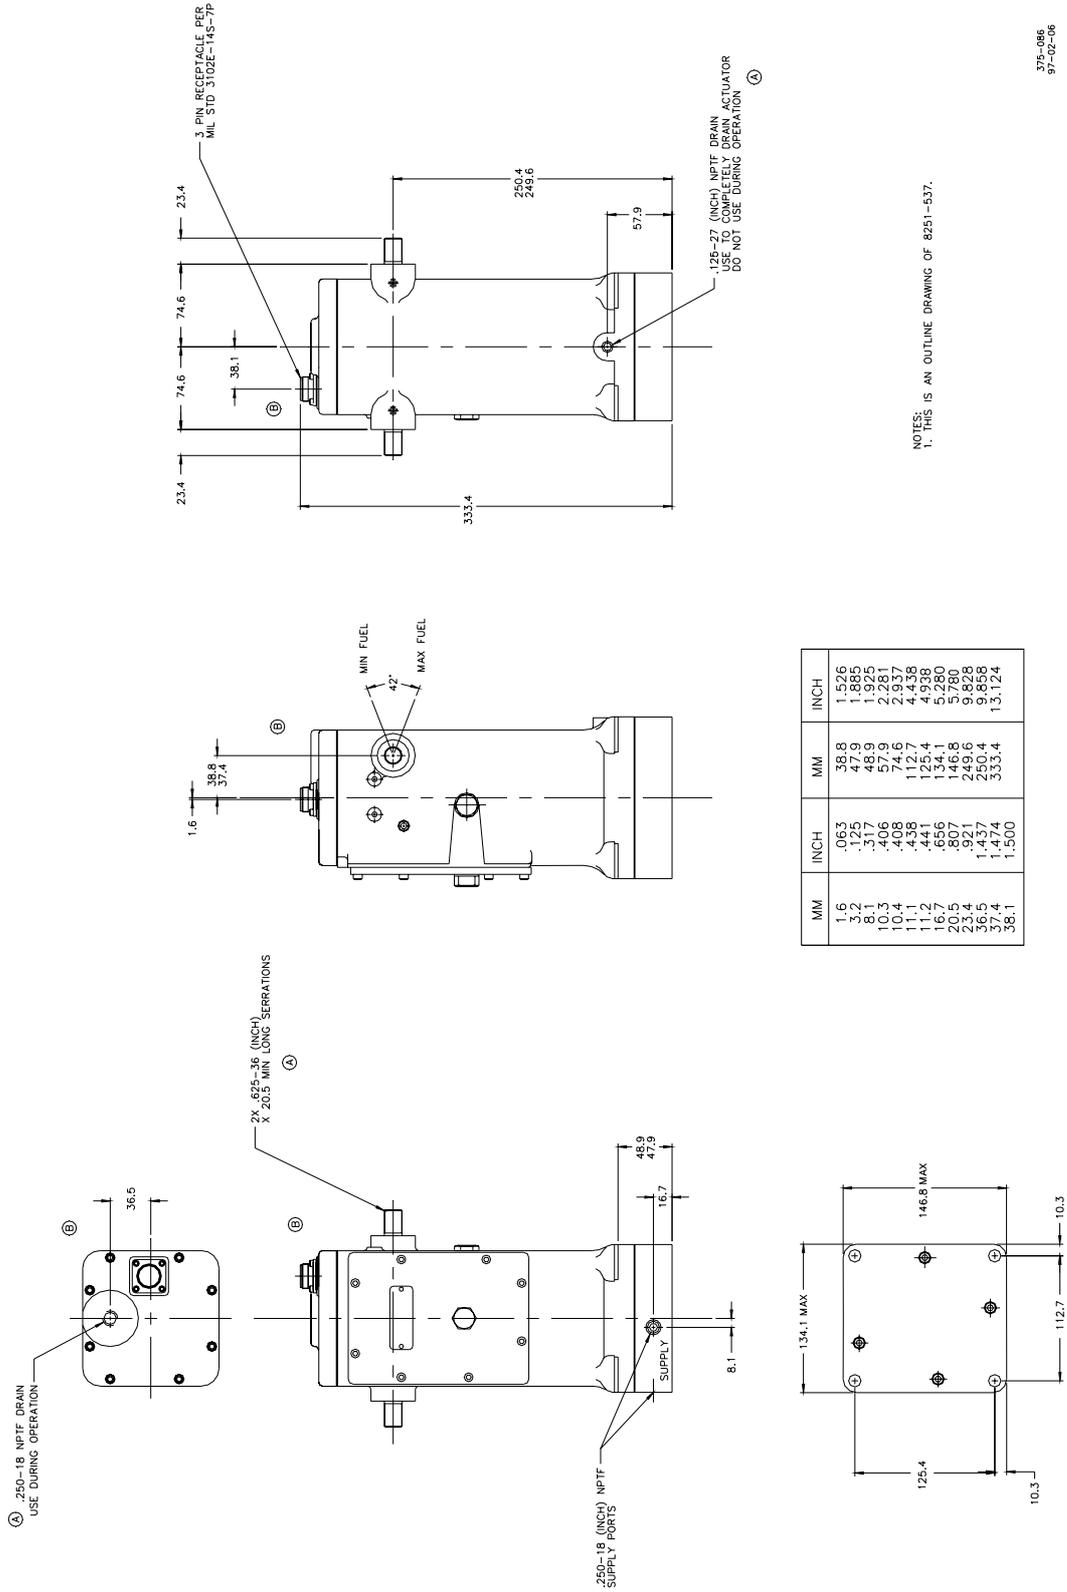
Чертёж общего вида UG-преобразователя
